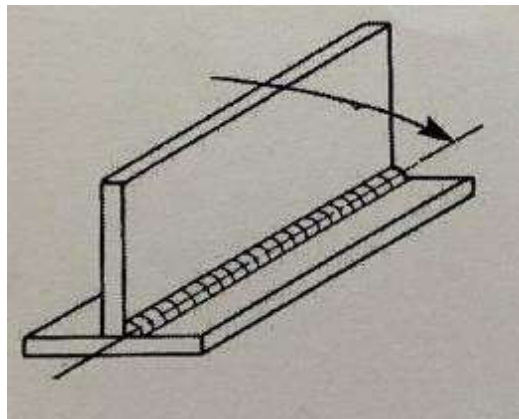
Soldadura de filete en unión entre láminas.
